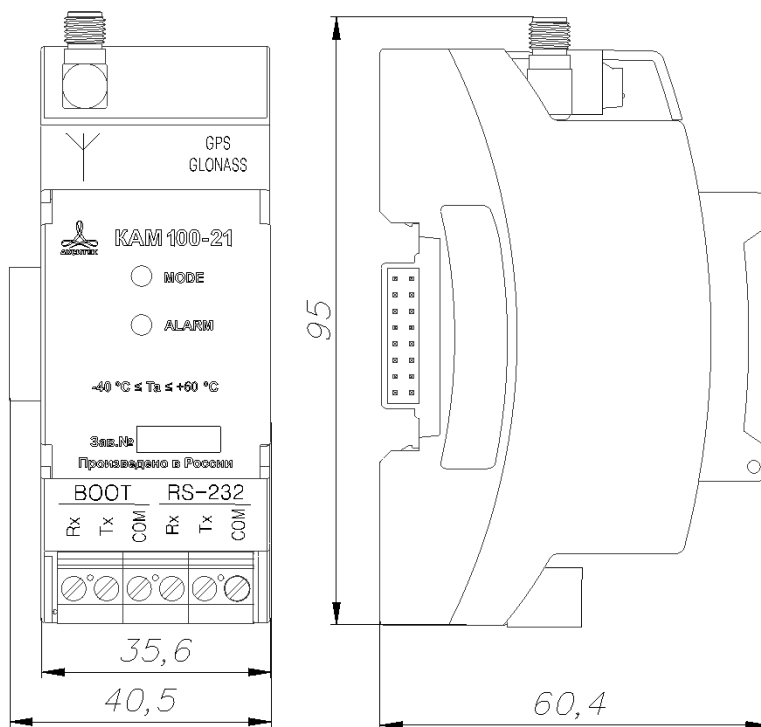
Внешний вид и габаритные размеры модуля геопозиционирования KAM100-21
